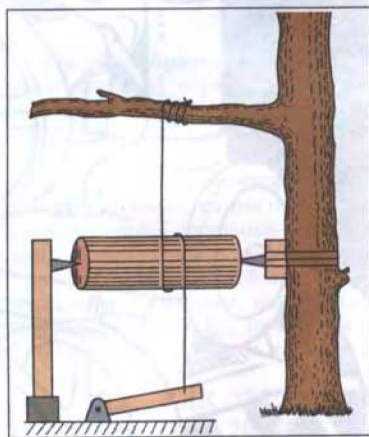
Схема примитивного токарного станка с «двигателями»: человек и упругая ветка
